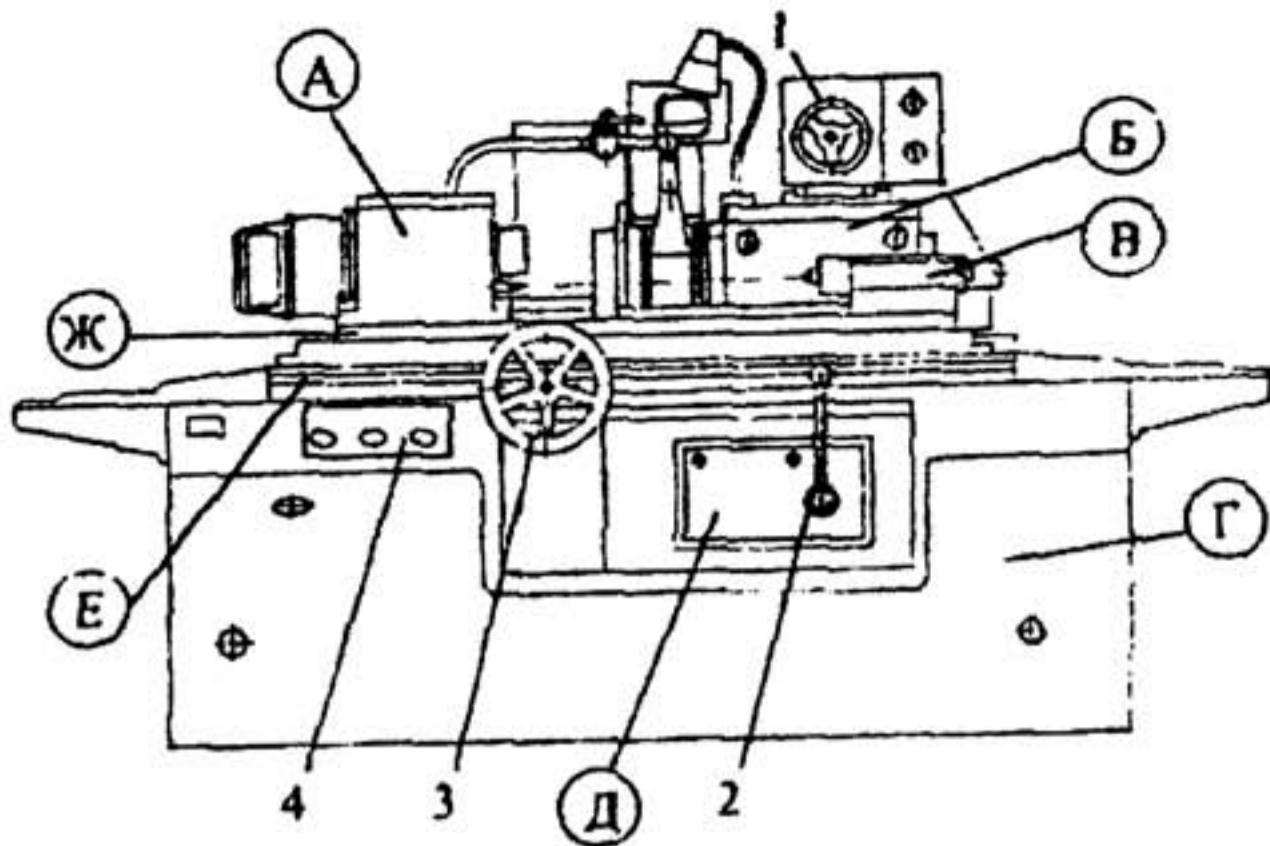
Общий вид круглошлифовального станка мод. 3Б151
